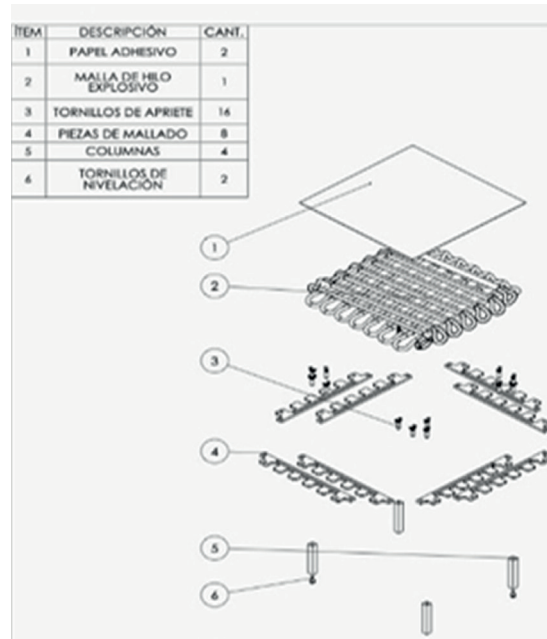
Plano y lista de materiales para la modificación y construcción de prototipo.
